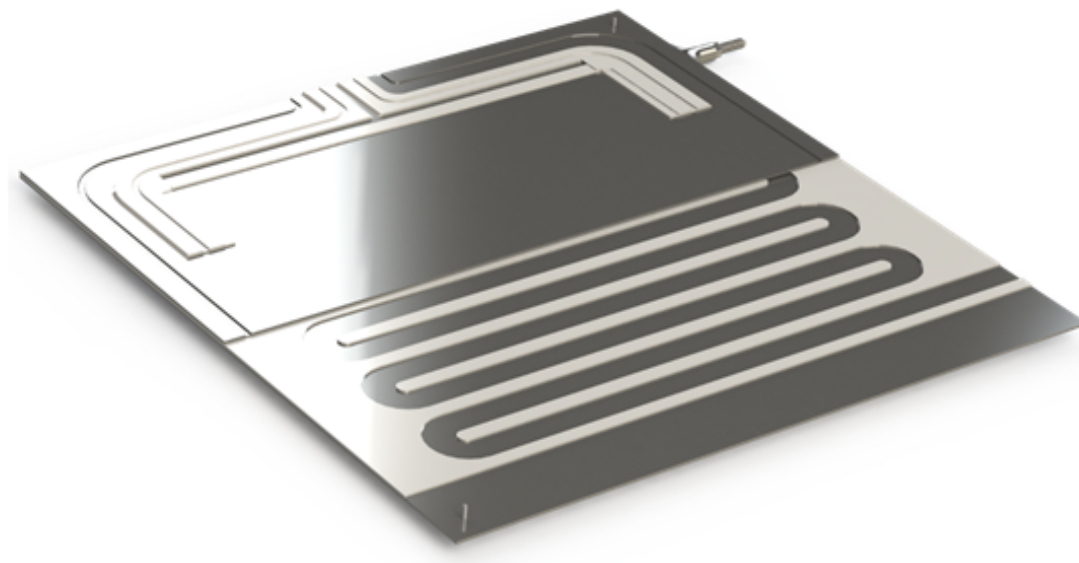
Exemple peau chauffante plane (vue en coupe)
